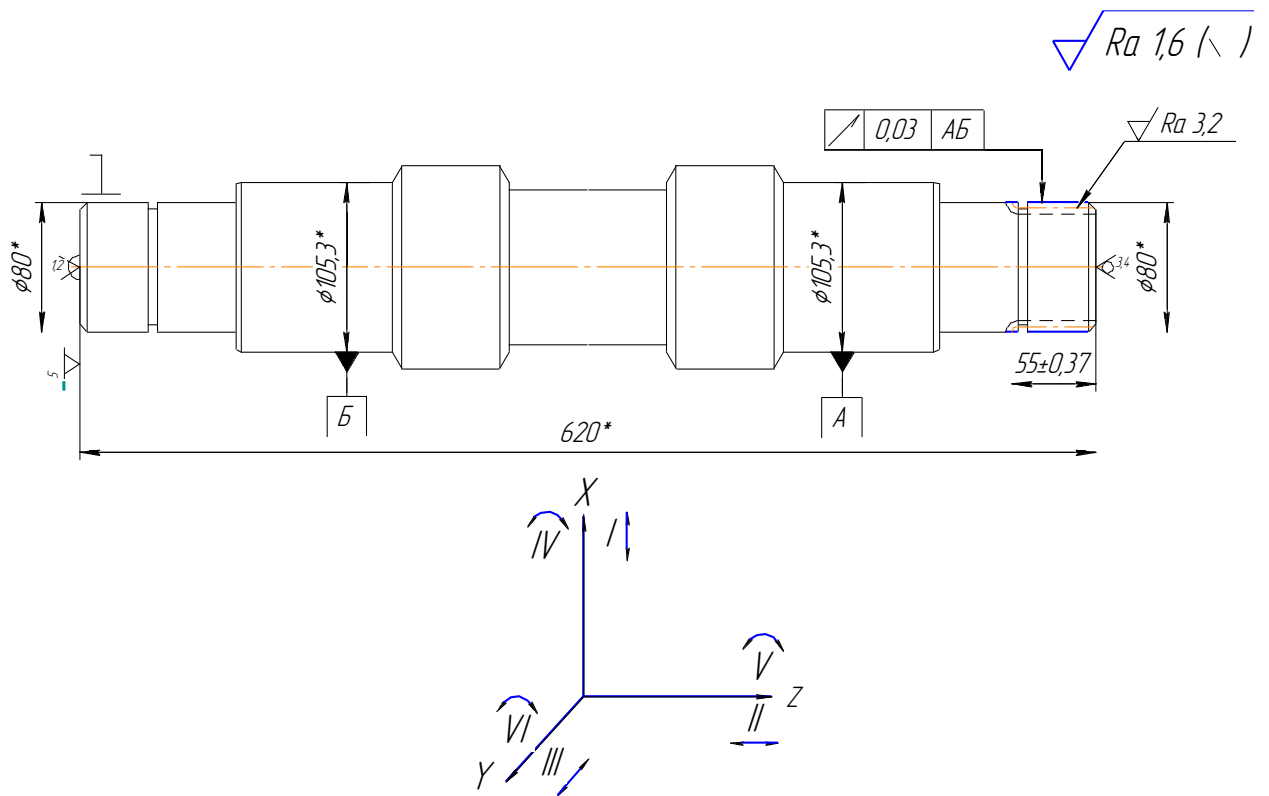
Схема базування Вала-шестерні на зубофрезерній операції 070
